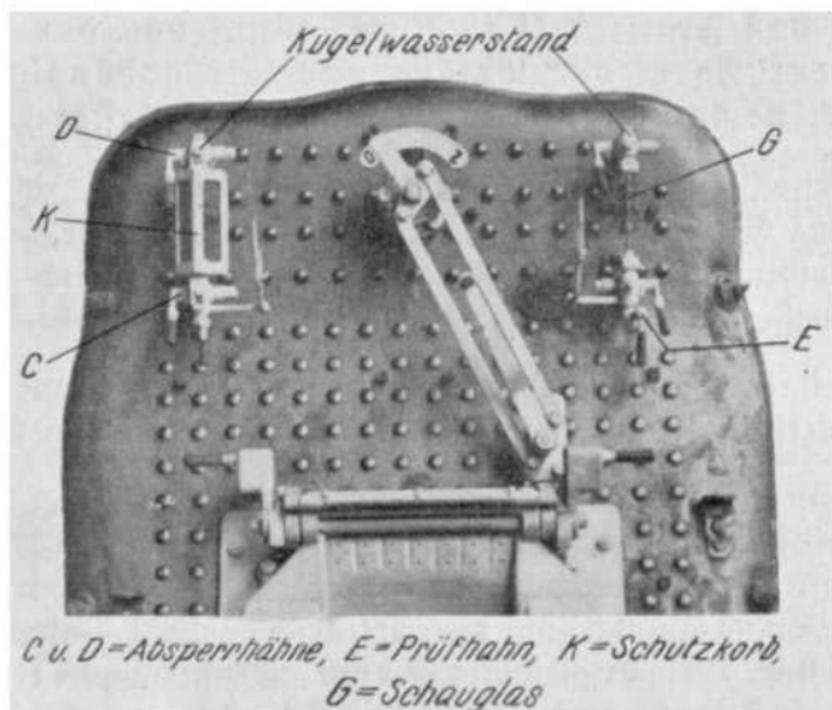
Hinterkesselrückwand mit Kugelwasserstand
